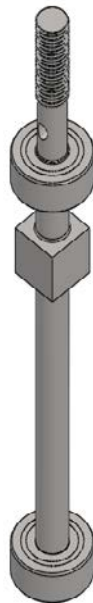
Cojinetes instalados en las posiciones B y C.
